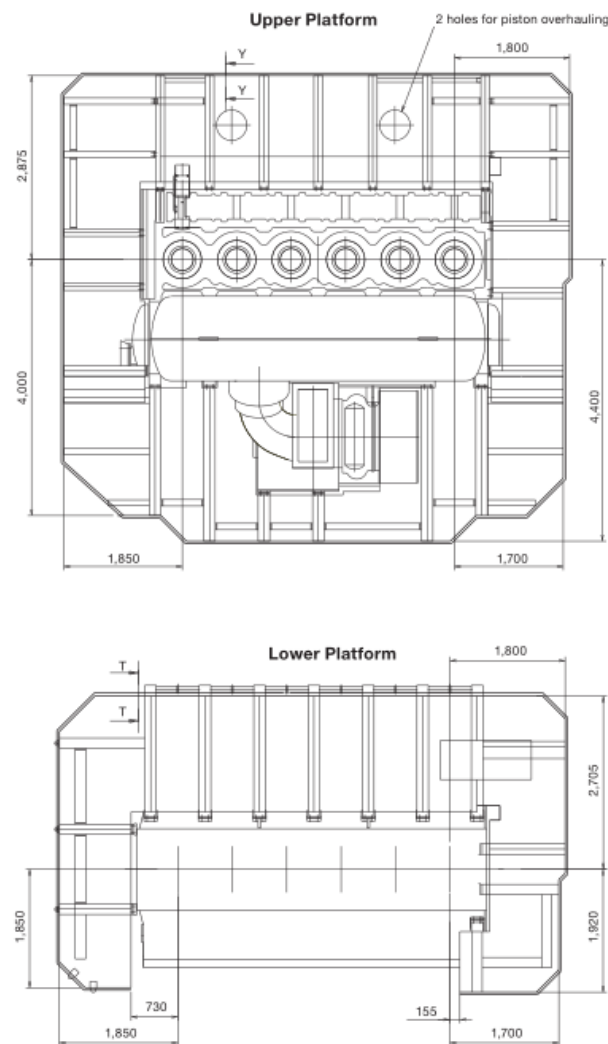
Розміри платформи для обслуговування двигуна S50ME-C8 з турбокомпресором на стороні випуску [8]
